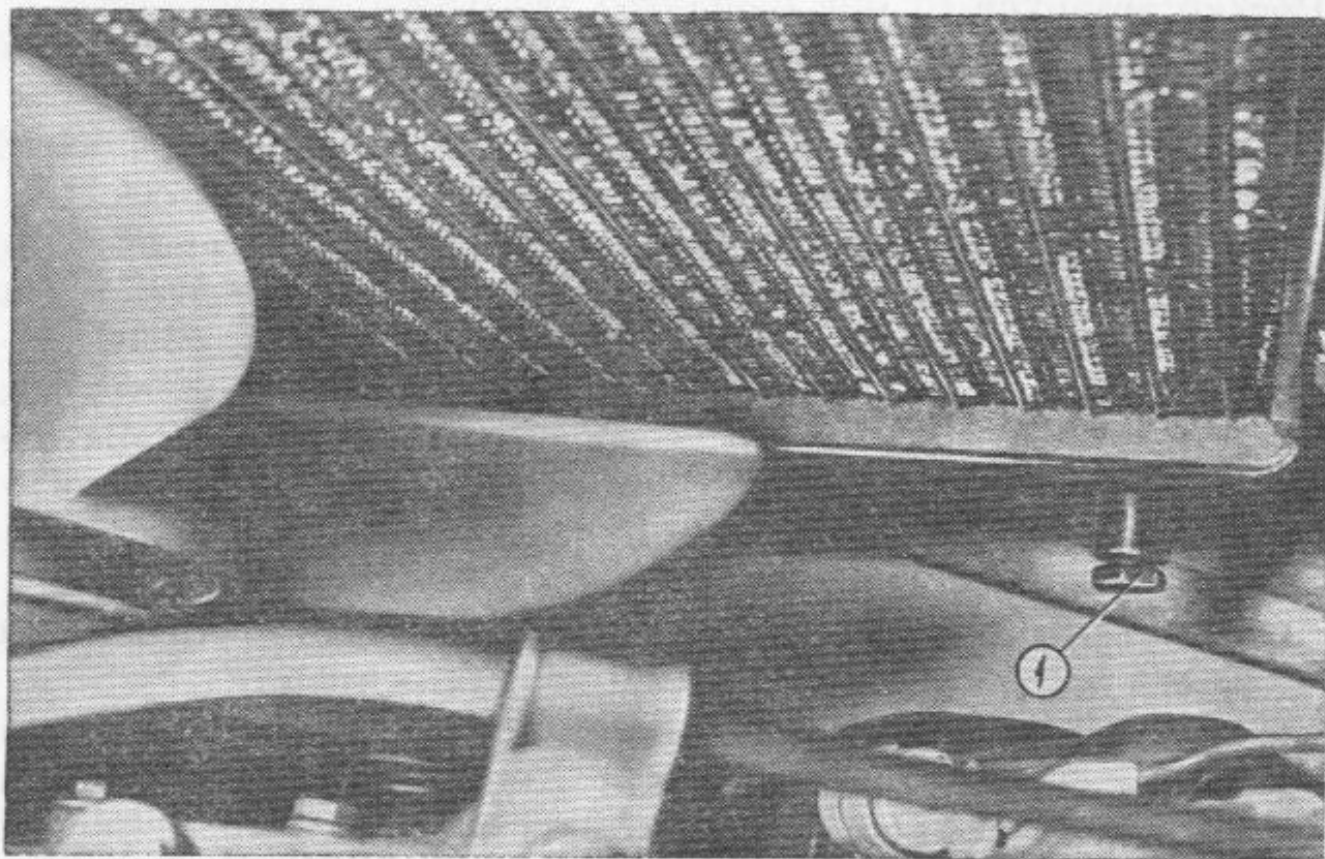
Anordnung der Ablasschraube am unteren Wasserkasten des Kühlers :
